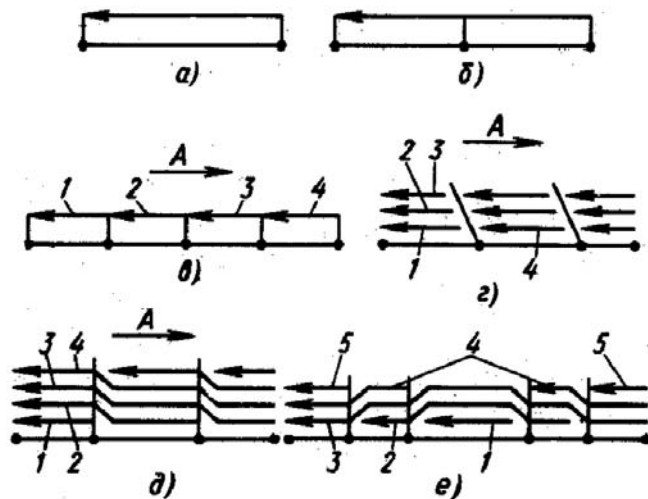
Сварка швов: а – напроход; б – от середины к концам; в – обратно-ступенчато; г – блоками; д – каскадом; е – горкой; А – направление заполнения разделки; стрелками указаны последовательность и направление сварки в каждом слое (1 – 5)
